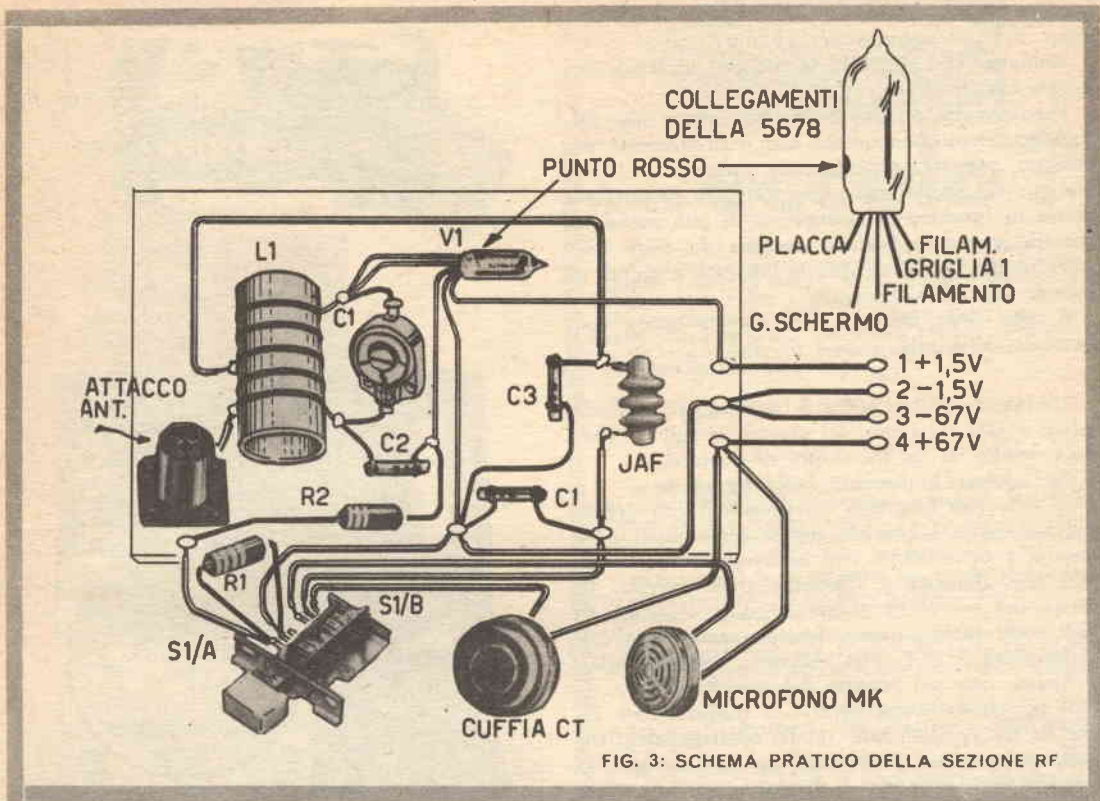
SCHEMA PRATICO DELLA SEZIONE RF
